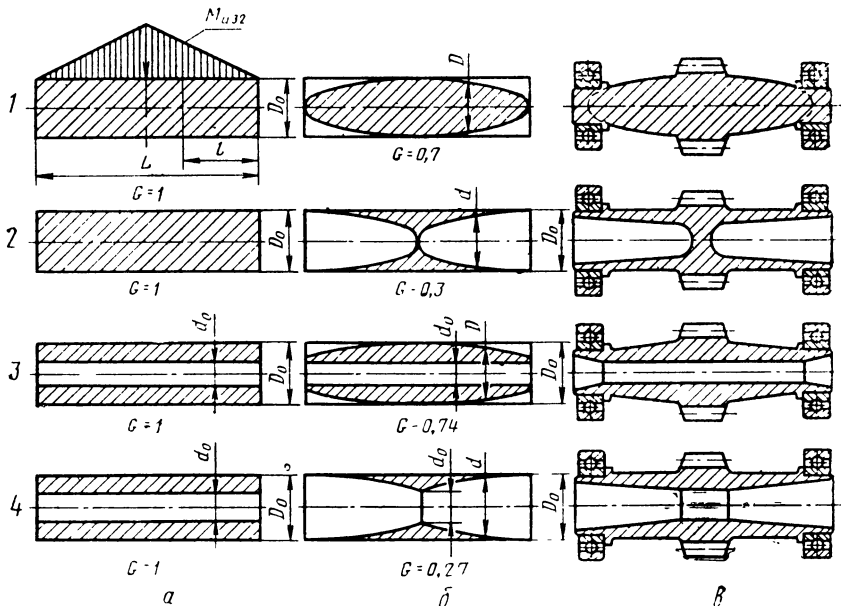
Способы придания цилиндрическим деталям равнопрочности: а — исходные формы; б — формы равнопрочной детали; в — реальная конструкция
